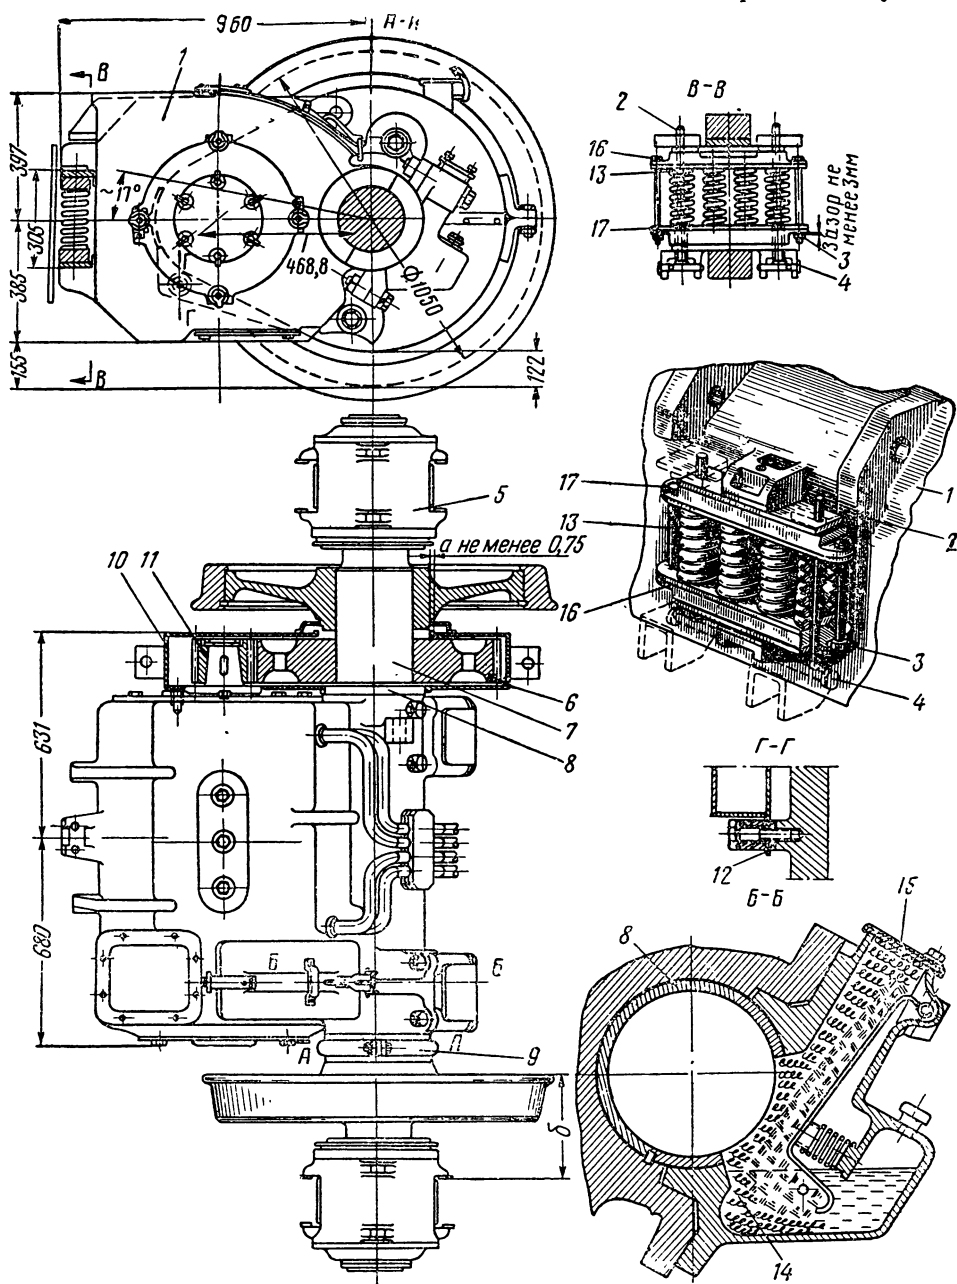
Расположение тягового электродвигателя на оси колесной пары:
